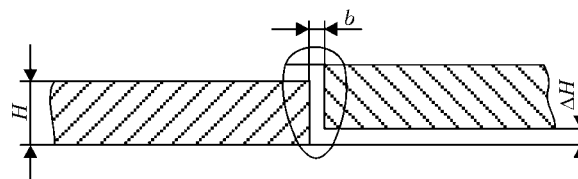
Схема стыкового соединения с зазором и смещением свариваемых кромок
